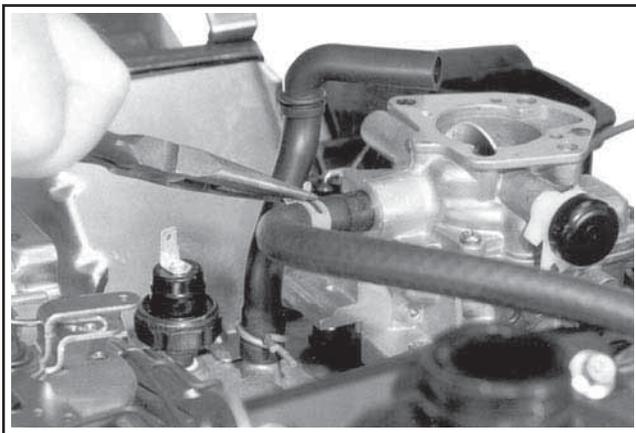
Déconnexion du tuyau d'entrée du carburant au carburateur.
